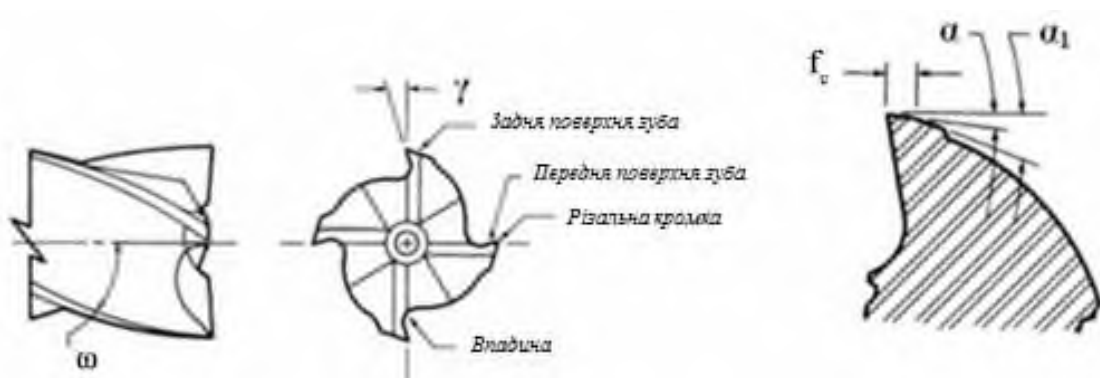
Геометрія заточування кінцевої фрези [13]
